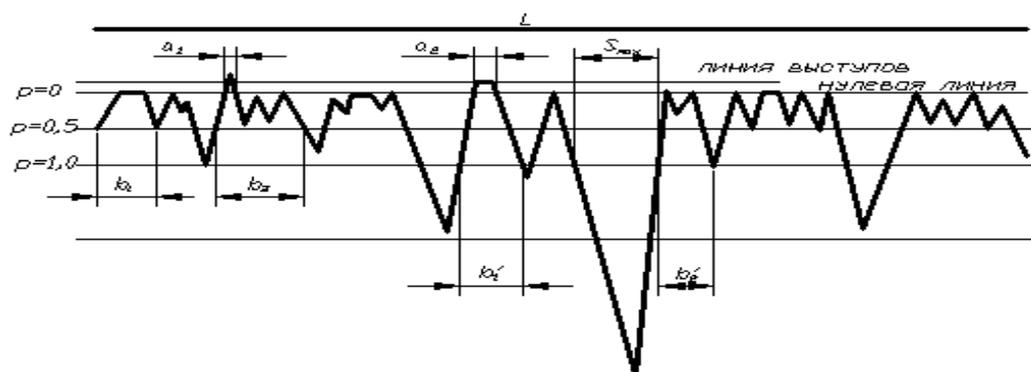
Профилограмма зеркала цилиндрической втулки
